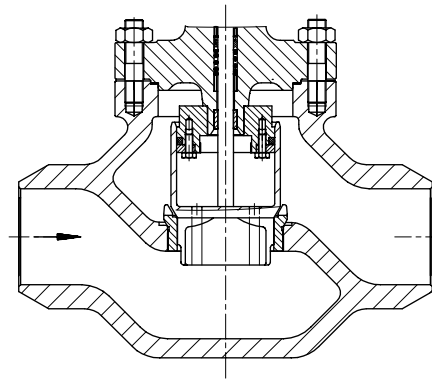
· Ventil Typ 3251 mit Anschweißenden und druckentlastetem Ventilkegel
